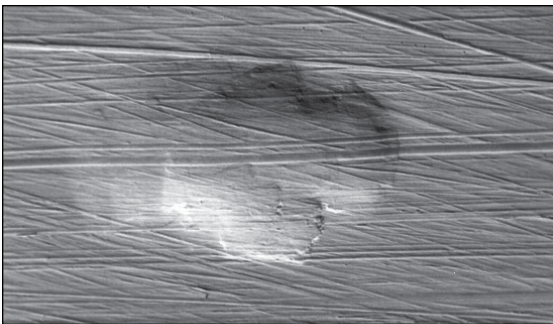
Pista interna (cono) de un rodamiento de rodillos cónicos astillada debido a abolladuras por contaminación.
